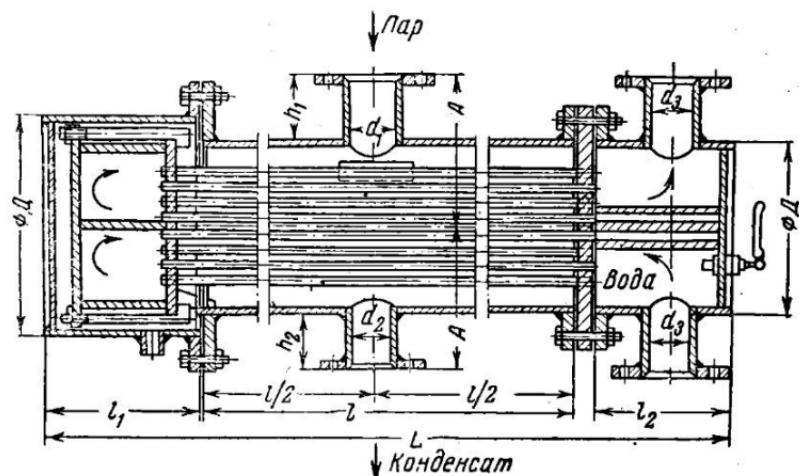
Четырехходовой пароводонагреватель конструкции
